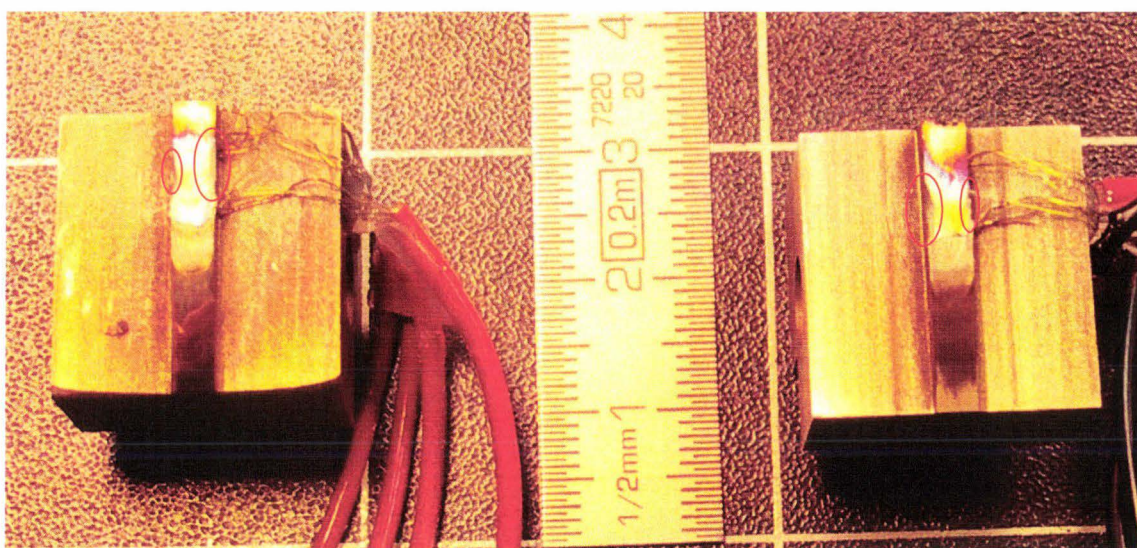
Écaillage des outils AISI M2 lors des essais préliminaires.
